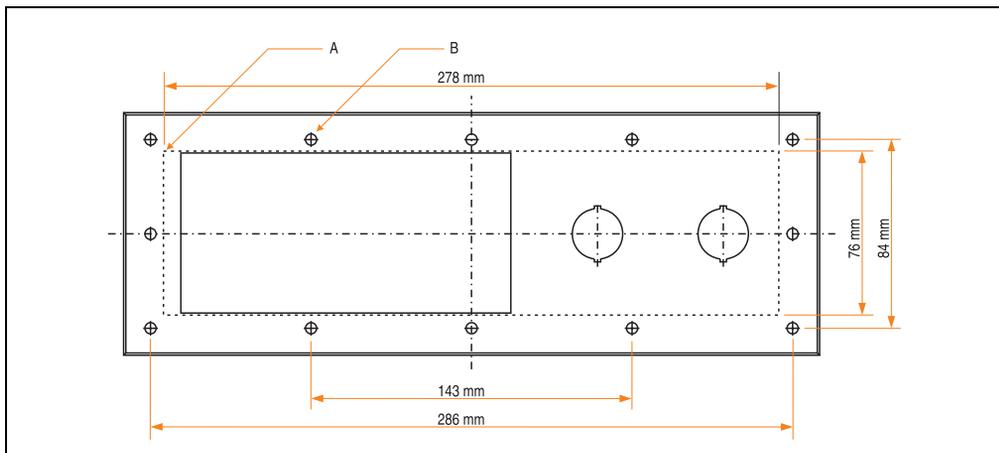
Frontplatte für externes Diskettenlaufwerk
